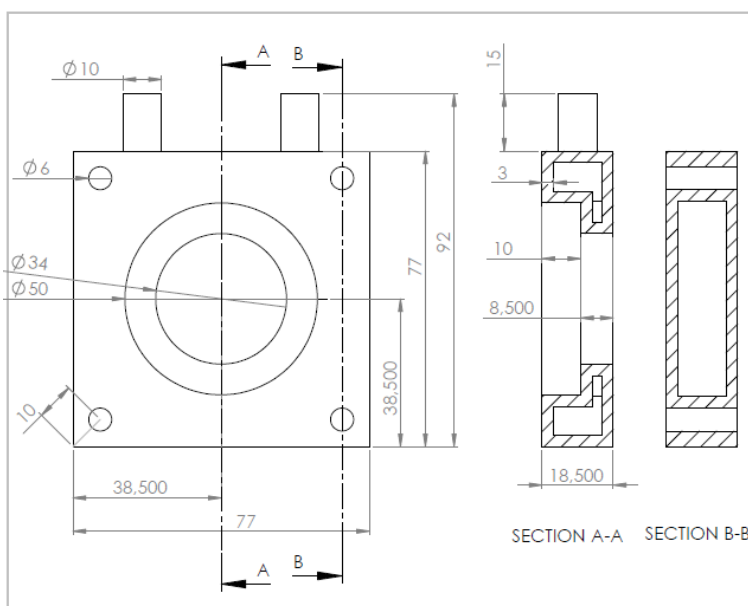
Desenho técnico do bloco 1. Vista frontal e cortes transversais das secções A-A e B-B. As paredes de aço têm 3 mm de espessura.
